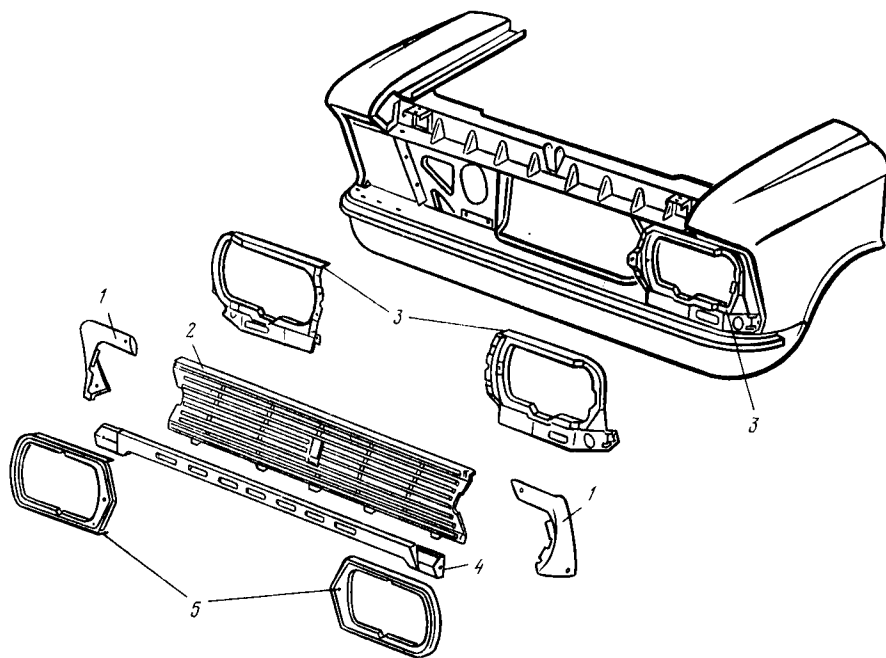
Детали облицовки радиатора автомобиля 412 с прямоугольными фарами: 1— декоративная накладка крыла (правая и левая); 2— облицовка радиатора; 3— стойка крепления фары (правая и левая); 4— брус облицовки радиатора в сборе; 5— накладка фары декоративная
